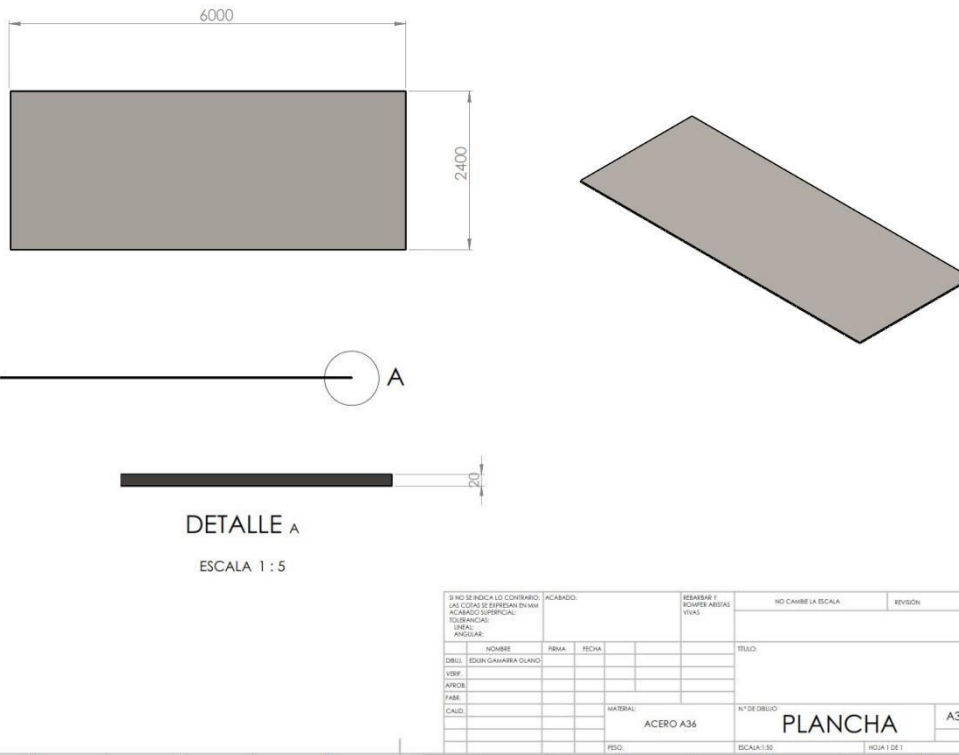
Dimensiones de la plancha metálica. Fuente
